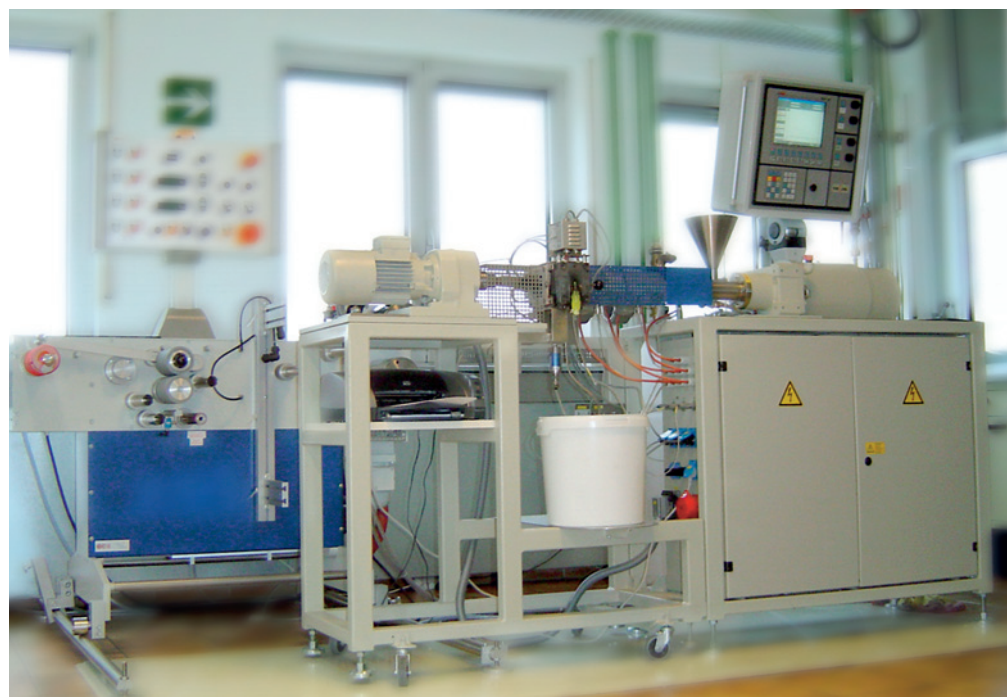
EN-13900-5-konformer Extruder im Labor der Herstellers
